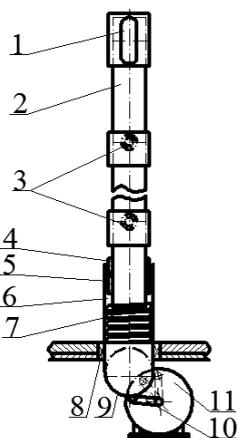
Встряхивающий механизм: 1 – сквозное отверстие; 2 – штатив; 3 – отверстия для фиксации сетчатых поддонов; 4 – прямоугольный выступ; 5 – канавка для вхождения прямоугольного выступа; 6 – цилиндрический стакан; 7 – противоударная пружина; 8 – металлический фиксатор; 9 – цилиндрическая канавка; 10 – палец; 11 – мотор-редуктор
